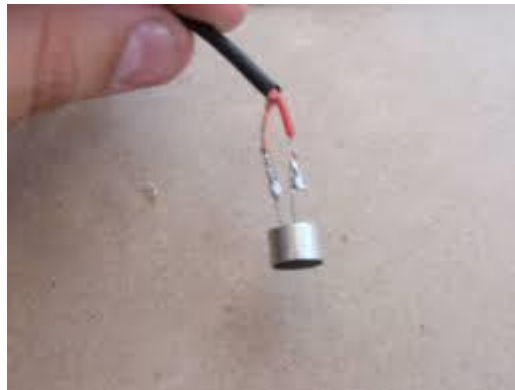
Cápsula soldada a cable de auriculares
